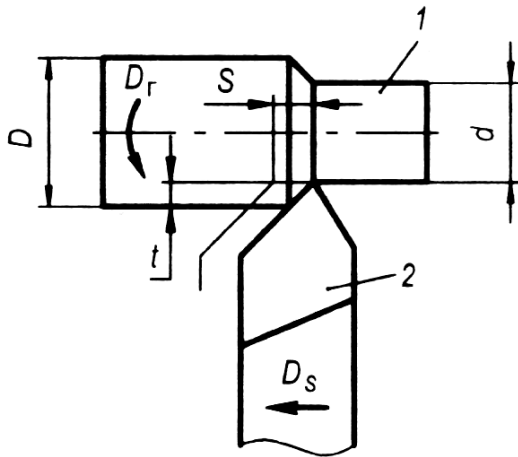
Елементи режиму різання при точінні: 1 - заготовка; 2 - різець; D_r - головний рух різання; D_s - рух подачі; t - глибина різання; S - подача; D і d - діаметри оброблюваної та обробленої поверхонь
